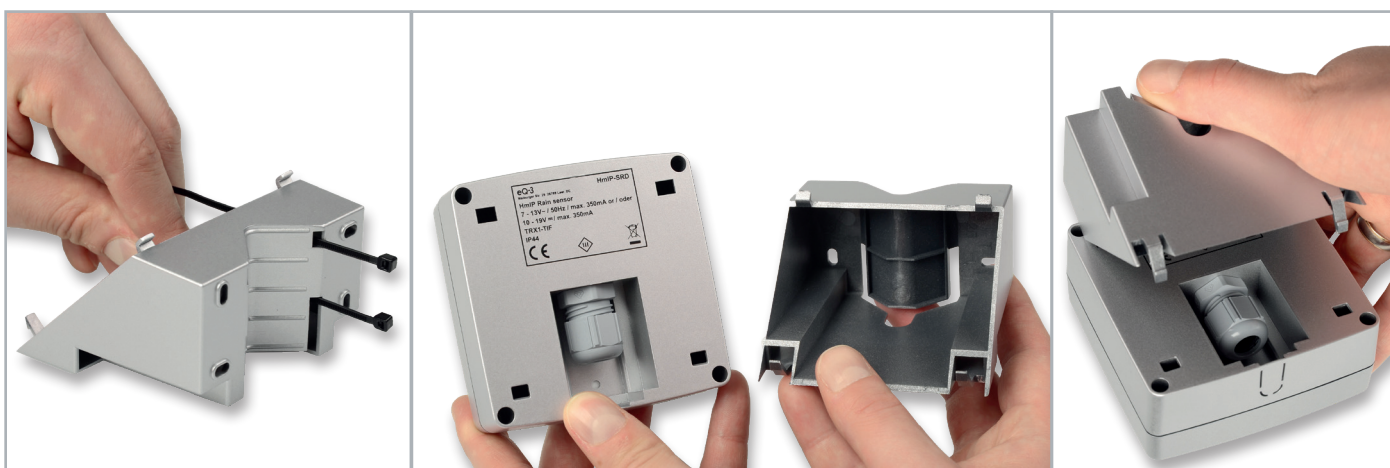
Nachdem man entweder, wie hier gezeigt, die Kabelbinder für die Mastbefestigung in die 45-Grad-Montageplatte eingesetzt oder die Montageplatte an einer senkrechten Fläche verschraubt hat, wird das Gerät in die Montageplatte eingesetzt: oben die beiden Haltenasen einsetzen, unten die Rastnasen einclippen.
